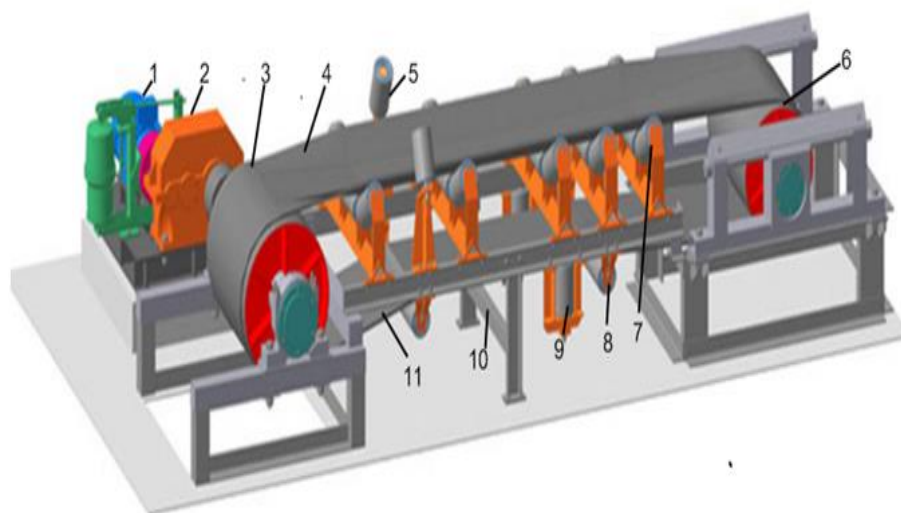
Будова стрічкового конвеєра : 1-приводний електродвигун, 2-редуктор приводу, 3-приводний барабан; 4-робоча стрічка конвеєра, 5-ролики проти сходу для робочої стрічки; 6-натяжний барабан, 7-підтримуючі ролики для робочої стрічки; 8-підтримуючі ролики для холостої стрічки, 9-ролики проти сходу для холостої стрічки, 10-конвеєрний став, 11-холоста стрічка конвеєра
